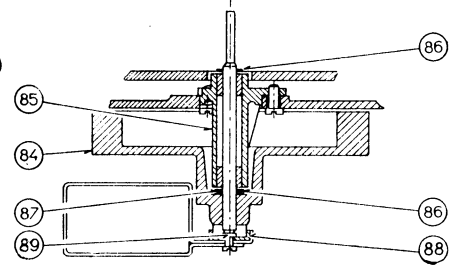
Náhradní součásti tlačítkové soupravy 30
